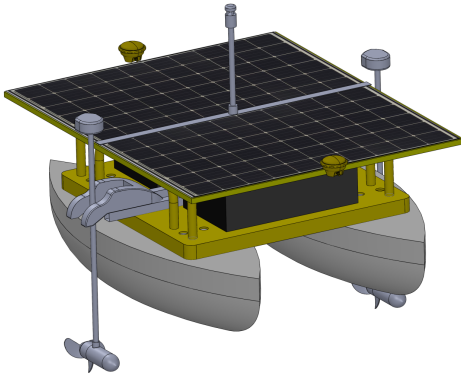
Modelado en CAD del ASV – Cheemkin.
